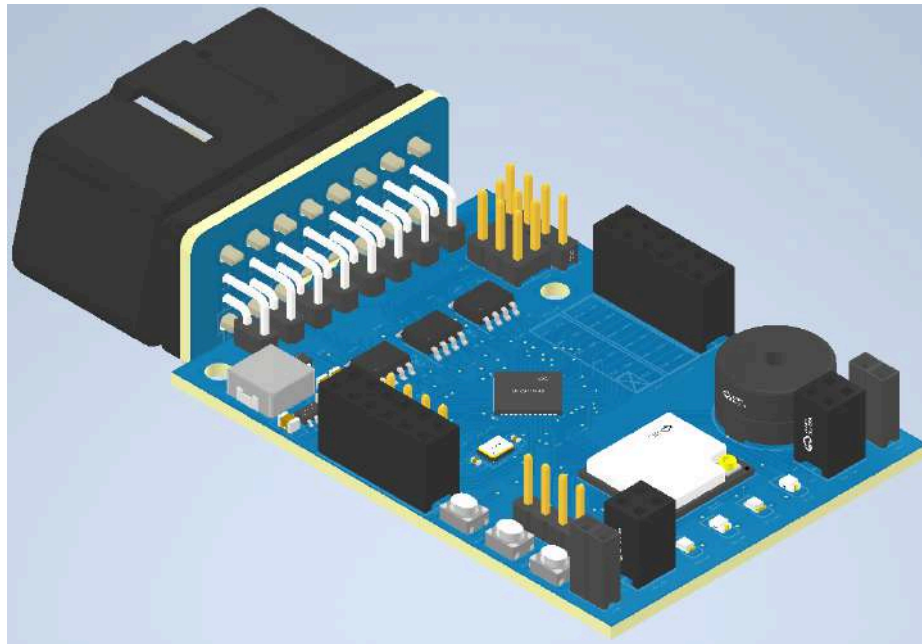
Ensamble 3D de la placa de desarrollo con el adaptador a 90° y el conector OBD-II del prototipo final.
